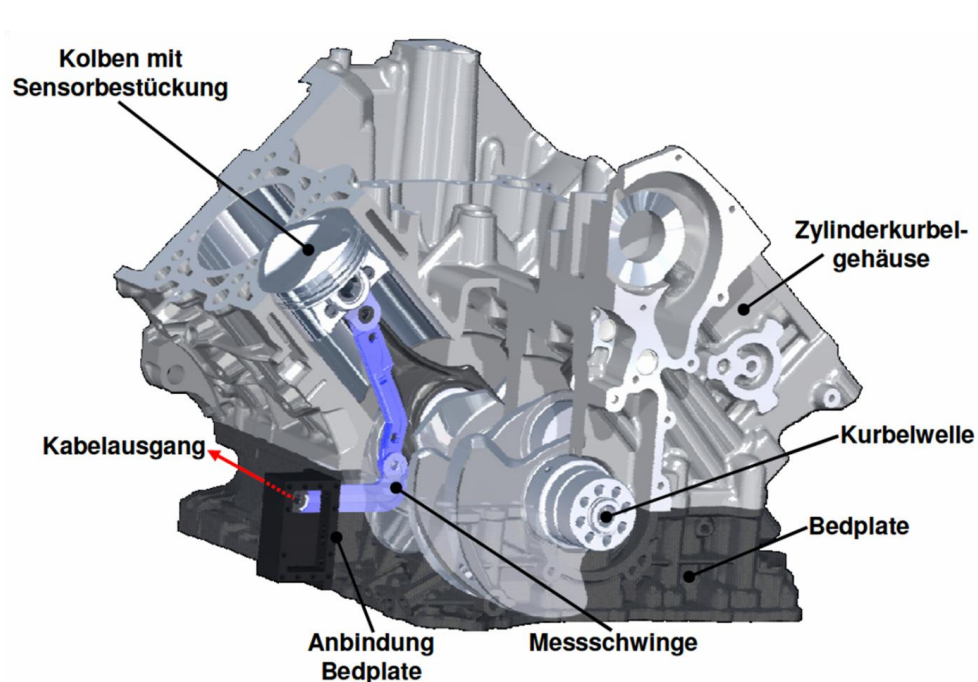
Einbau einer Messschwinde im Vollmotor [32]
